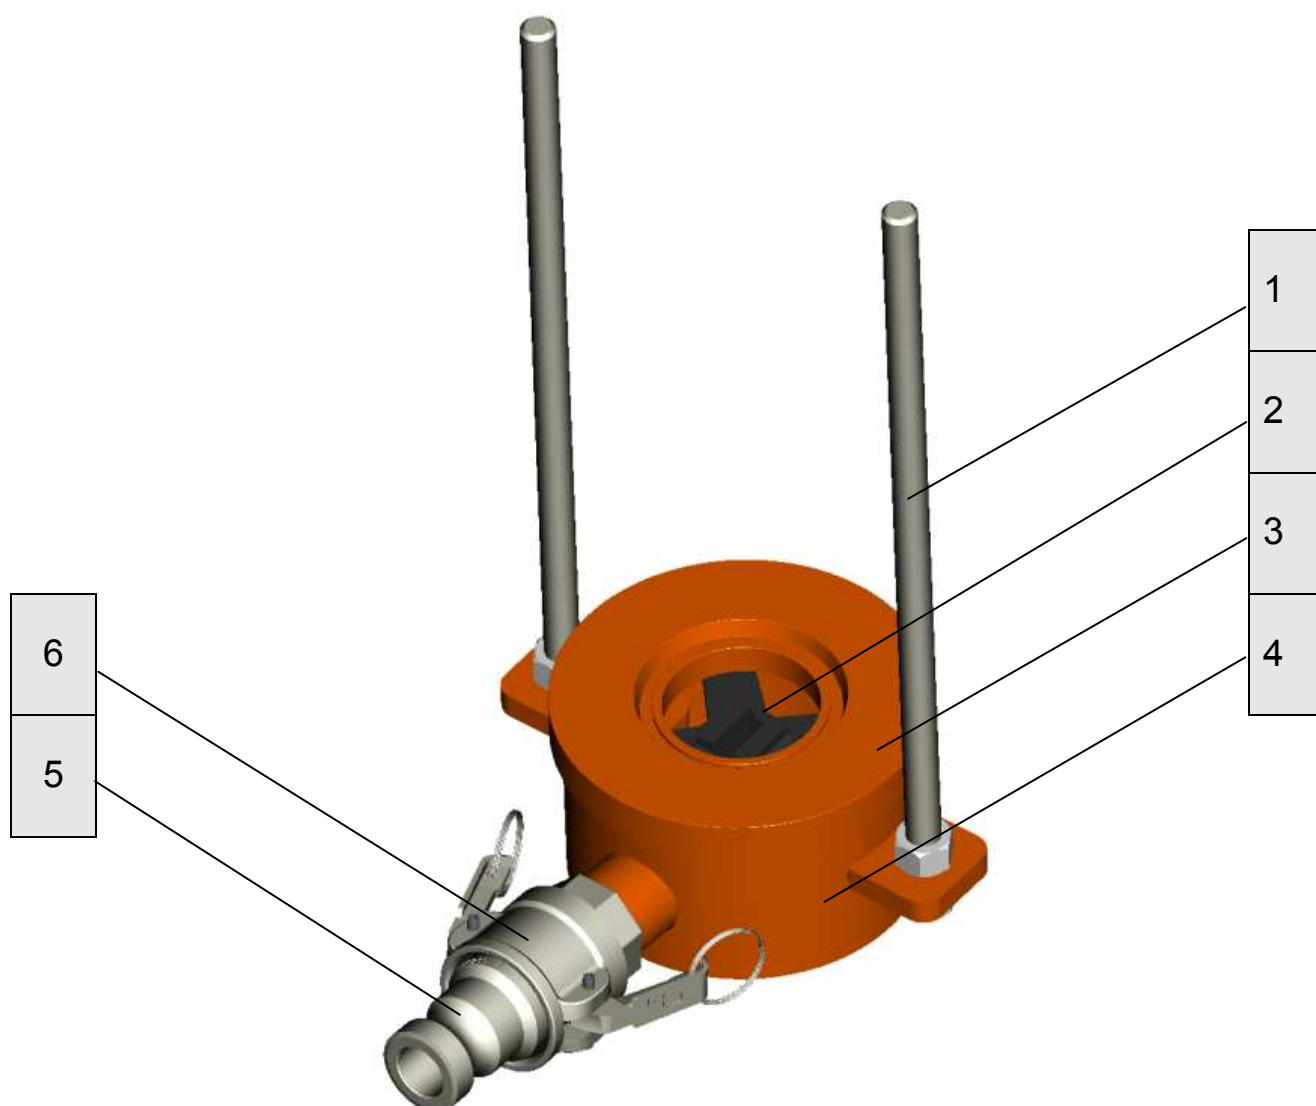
Vue d'ensemble Rotomix 20 11 80 00
